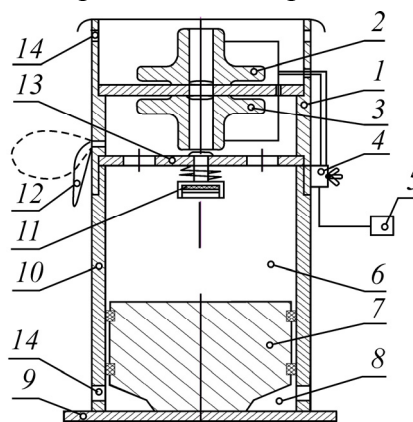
Схема КВУМ-3: 1 — съемный силовой блок; 2, 3 — верхний и нижний компрессионно-вакуумный механизм; 4 — трехпозиционный переключатель; 5 — источник тока; 6 — камера рабочего хода; 7 — ударник; 8 — нижняя камера; 9 — рабочий инструмент; 10 — корпус; 11 — магнит; 12 — ресивер; 13 — диск; 14 — всасывающие и выхлопные отверстия
